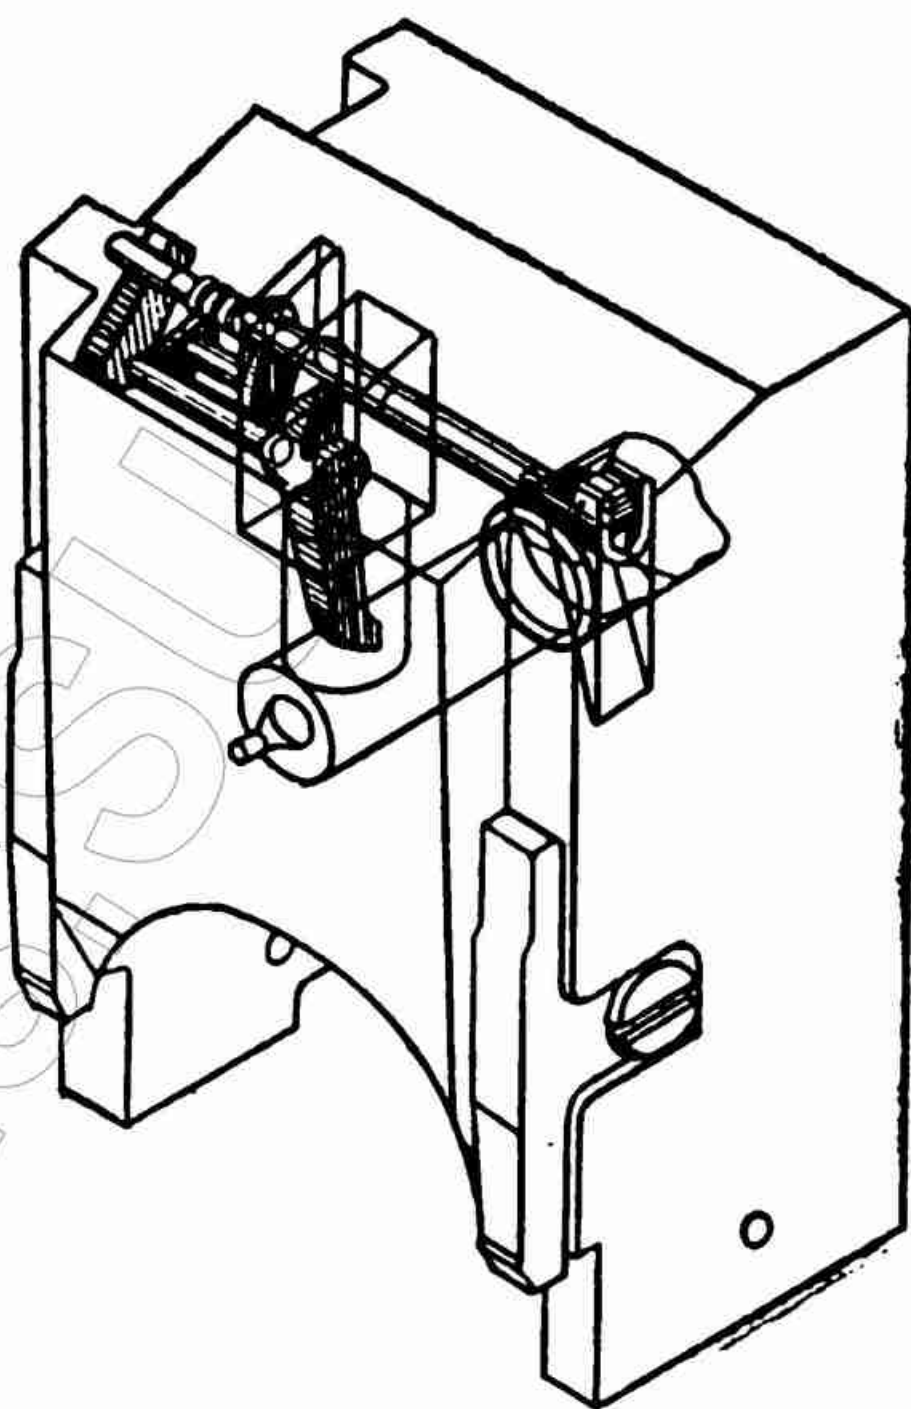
Положение деталей ударного и предохранительного механизмов при сборке (четвертая операция)
